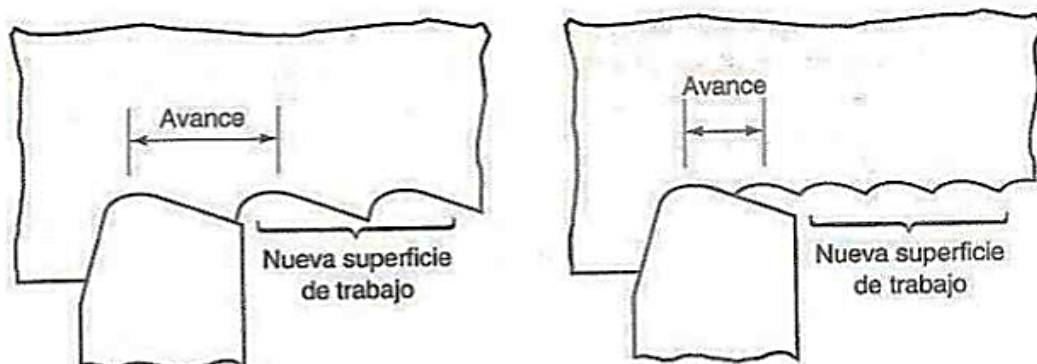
Rugosidad generada por: Herramienta de corte con filo y herramienta de corte con radio de punta.
